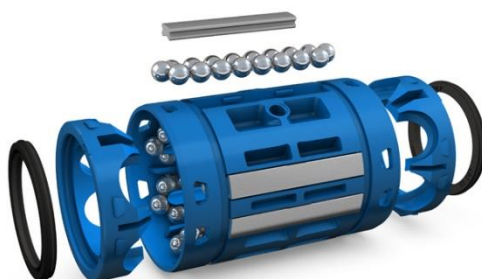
Направляющие дорожек качения и резервуар смазки
